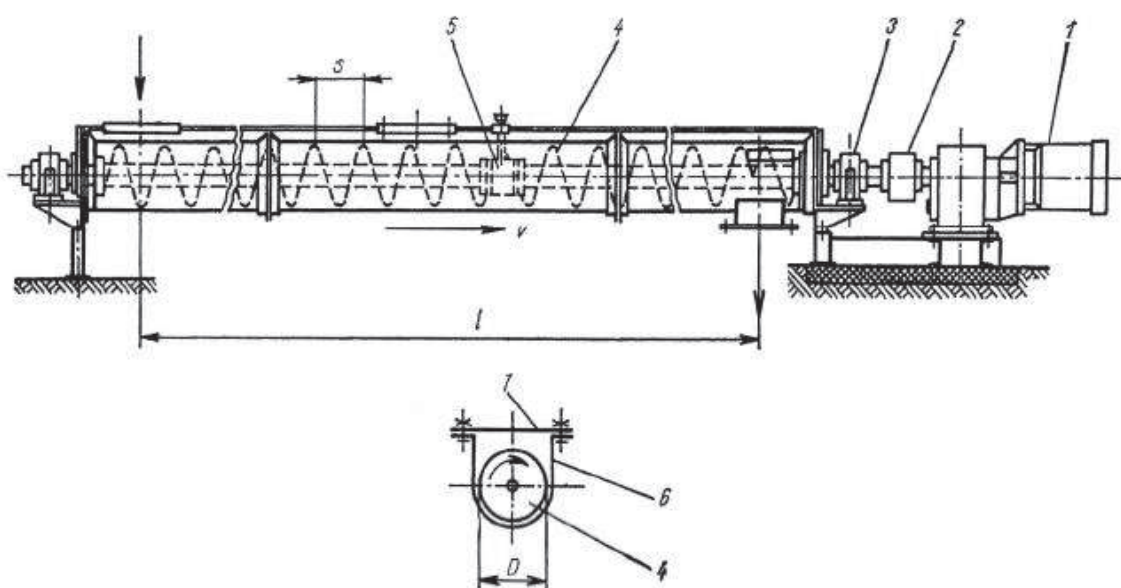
Rozhrabávač na dřevní štěrku [8]
